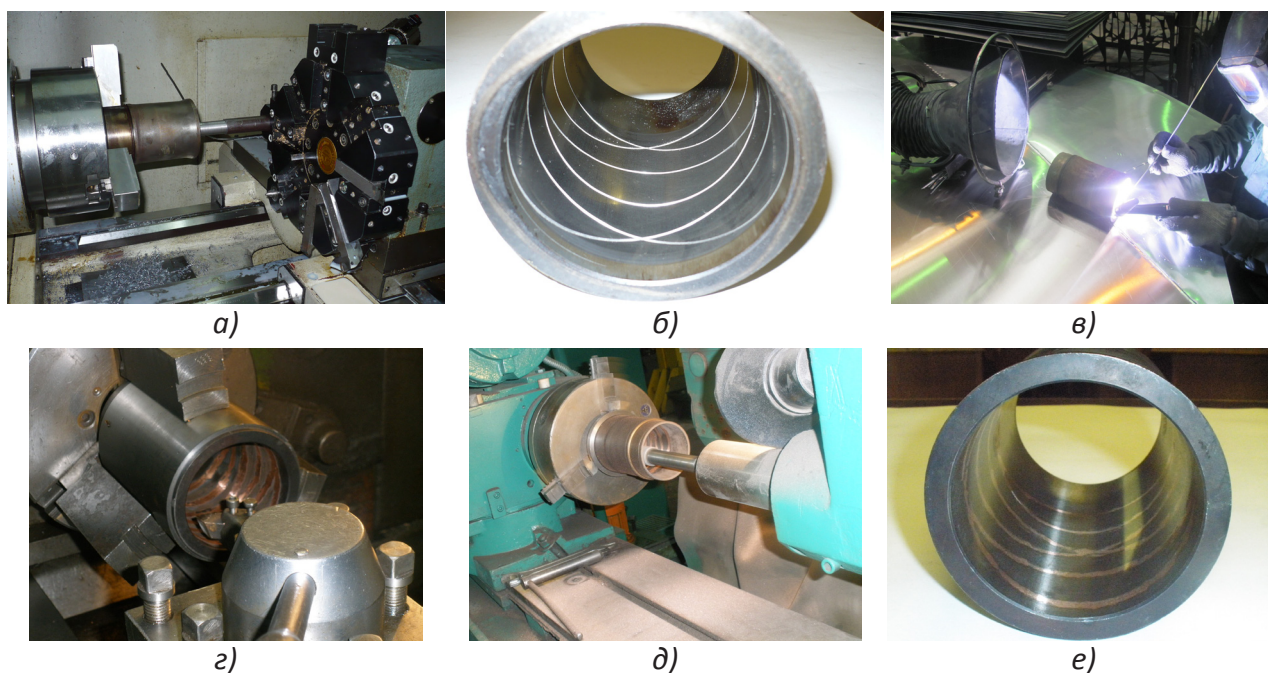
Технологический процесс изготовления металлизированной медью гильзы цилиндров: а) нарезка кольцевых канавок; б) гильза с нарезанными кольцевыми канавками; в) наплавка канавок медью; г) зачистка внутренней поверхности; д) шлифование внутренней поверхности; е) металлизированная гильза цилиндров
